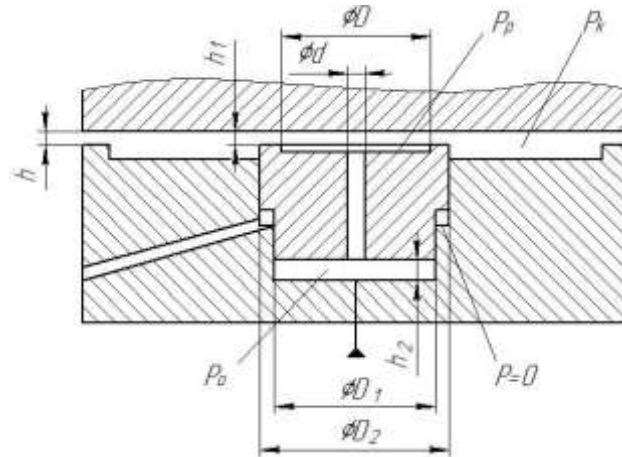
Конструкція незамкнутої гідростатичної напрямної з однопотоковими плаваючими плунжерними регуляторами активного нагнітання робочої рідини
